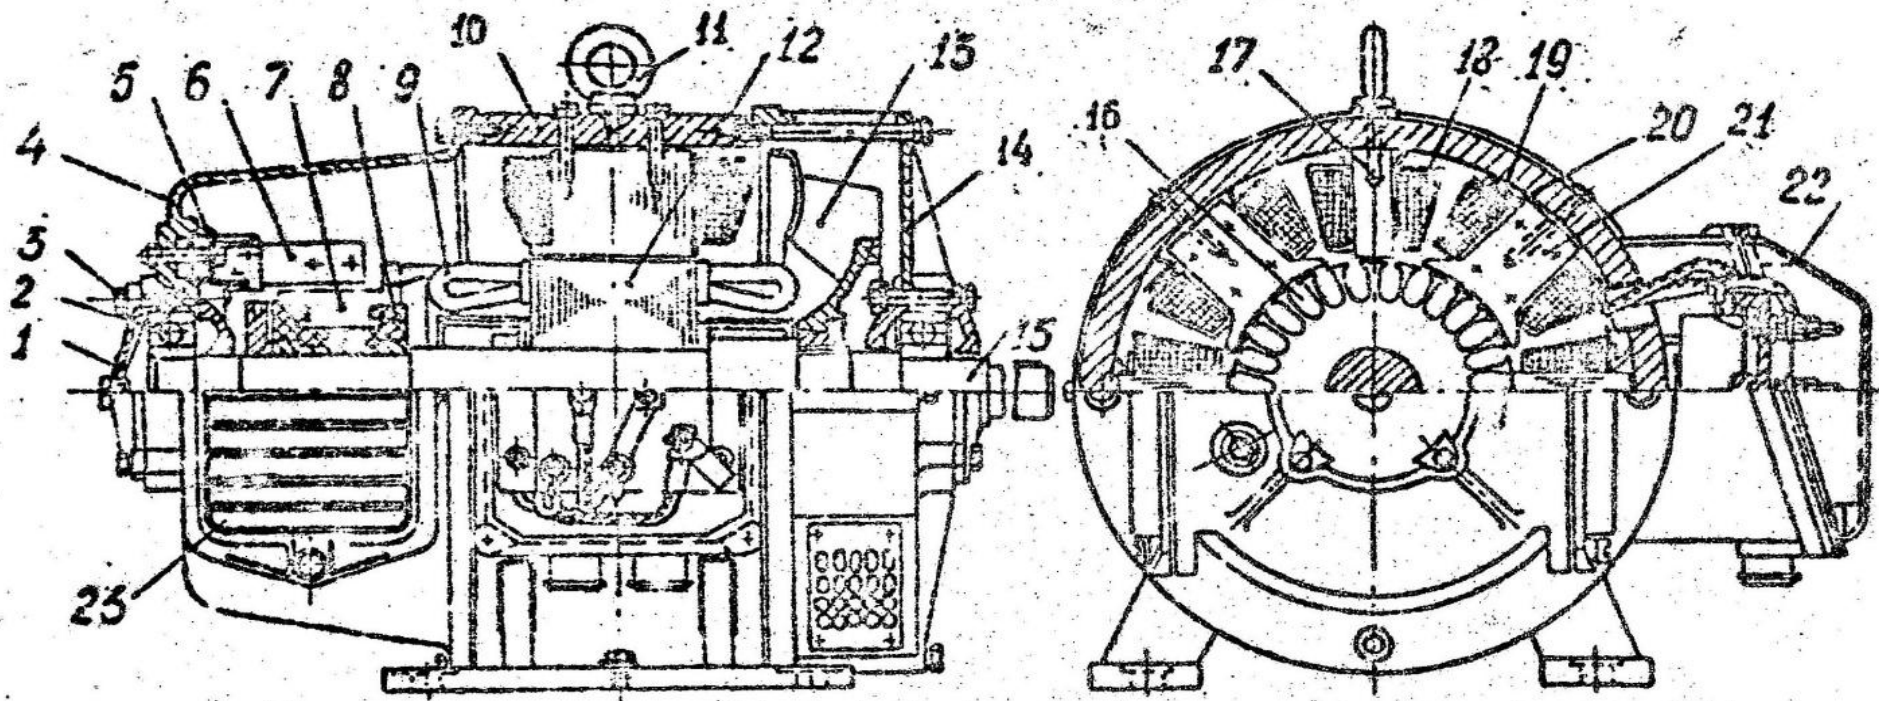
Продольный и поперечный разрезы машины постоянного тока серии П: 1 - крышка подшипника; 2 - шариковый подшипник; 3 - болт траверсы; 4 - передний подшипниковый щит; 5 - траверса; 6 - палец щеткодержателя; 7 - коллекторная пластина; 8 - пластмасса; 9 - лобовые части обмотки; 10 - ярмо; 11 - рым; 12 - сердечник ротора; 13 - вентилятор; 14 - задний подшипниковый щит; 15 - вал; 16 - паз ротора; 17 - сердечник дополнительного полюса; 18 - катушка дополнительного полюса; 19 - последовательная обмотка возбуждения; 20 - параллельная обмотка возбуждения; 21 - сердечник главного полюса; 22 - коробка выводов; 23 - щиток
